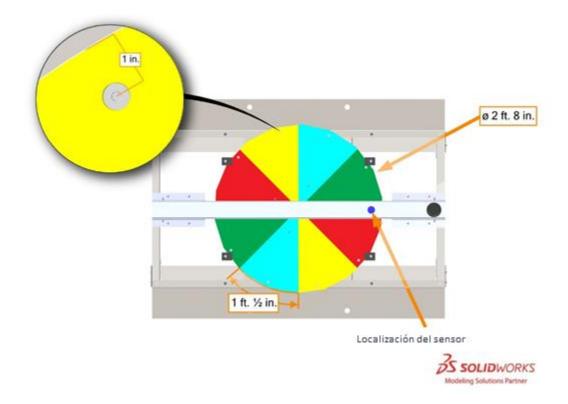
dimensiones de la TRINCHERA y del PANEL DE CONTROL
